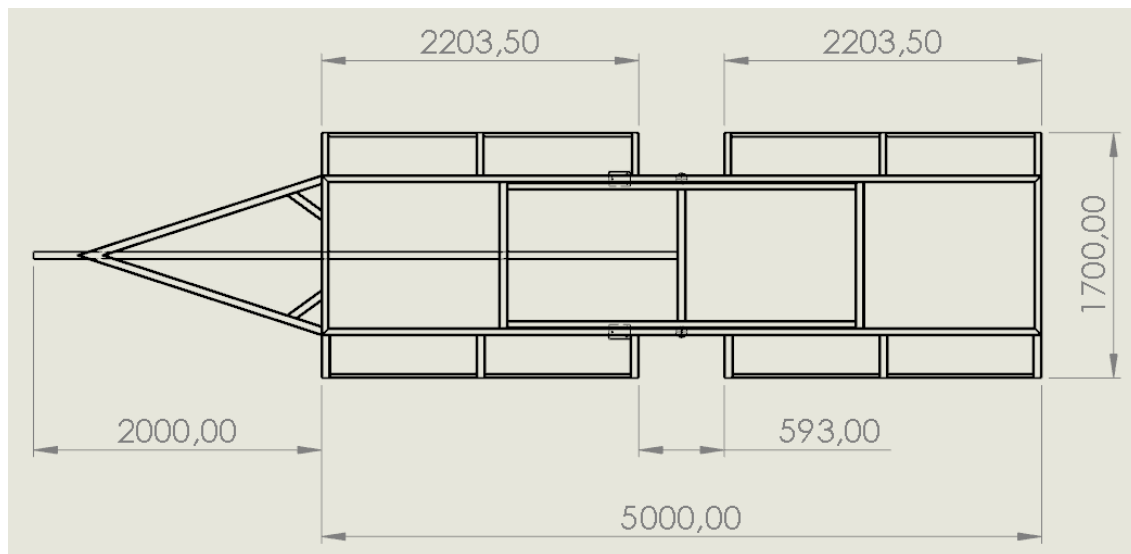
Vista inferior do posicionamento da chapa de fixação do eixo.
